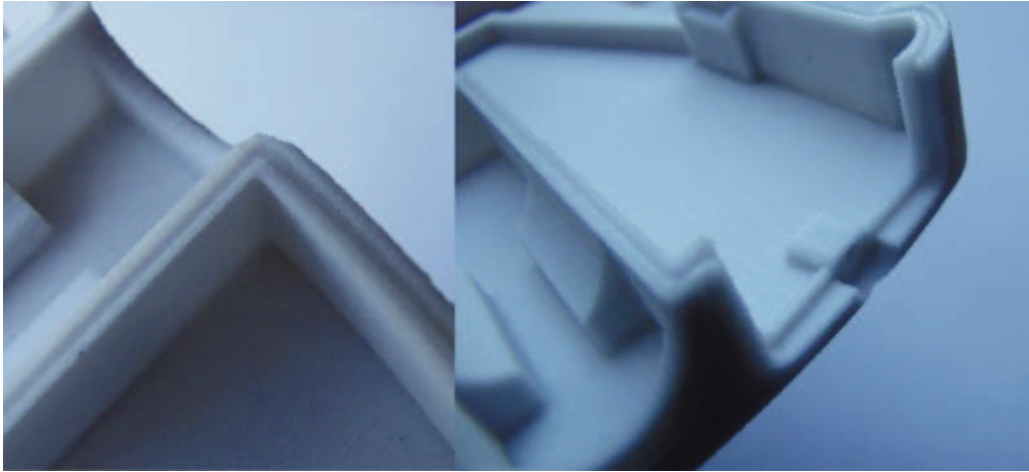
Vista pormenorizada dos detalhes impressos tridimensionalmente
